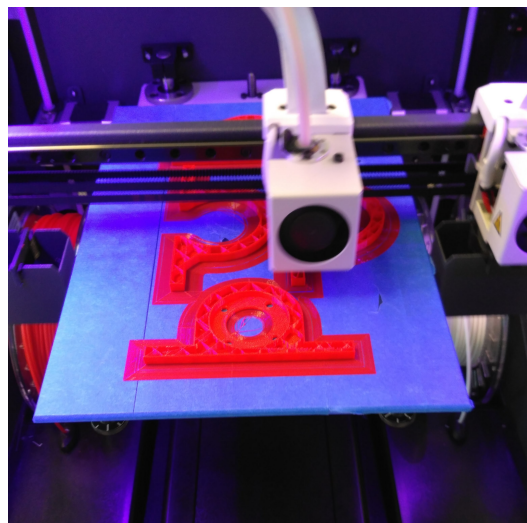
Impressão 3D dos Suportes dos Motores.
